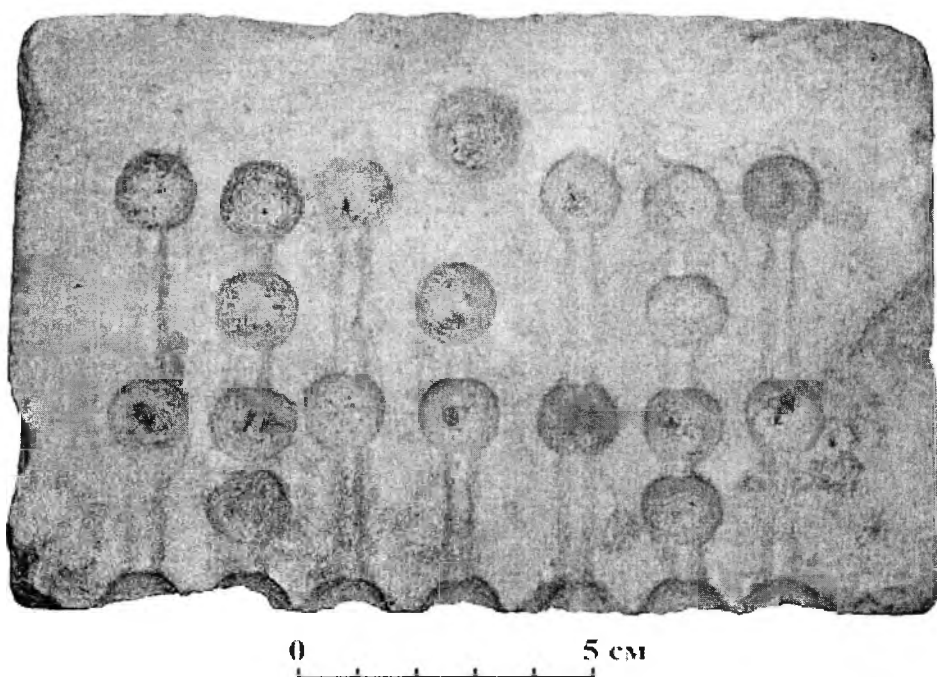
Створки формы для отливки пуль калибром 12,8 мм.
